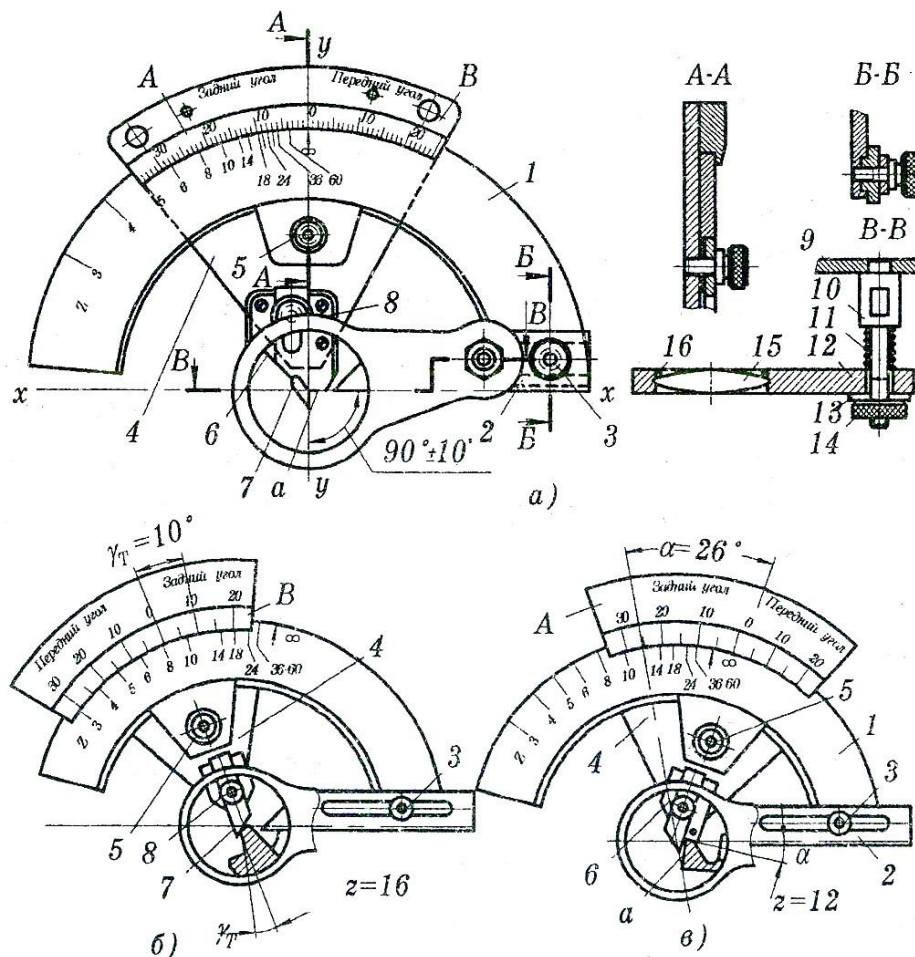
Угломер конструкции Бабчиницера: а - конструкция прибора; бив - измерение переднего и заднего углов: 1 - дуга с равномерной шкалой Z ; 2 - линейка; 3 - винт; 4 - сектор; 5 - винт; 6 - пластина; 7 - паз; 8 - винт прибора; 9 - основание; 10 - кронштейн; 11 - пружина; 12 - оправка; 13 - шайба; 14 - гайка; 15 - линза; 16 - пружина съёмного оптического устройства
